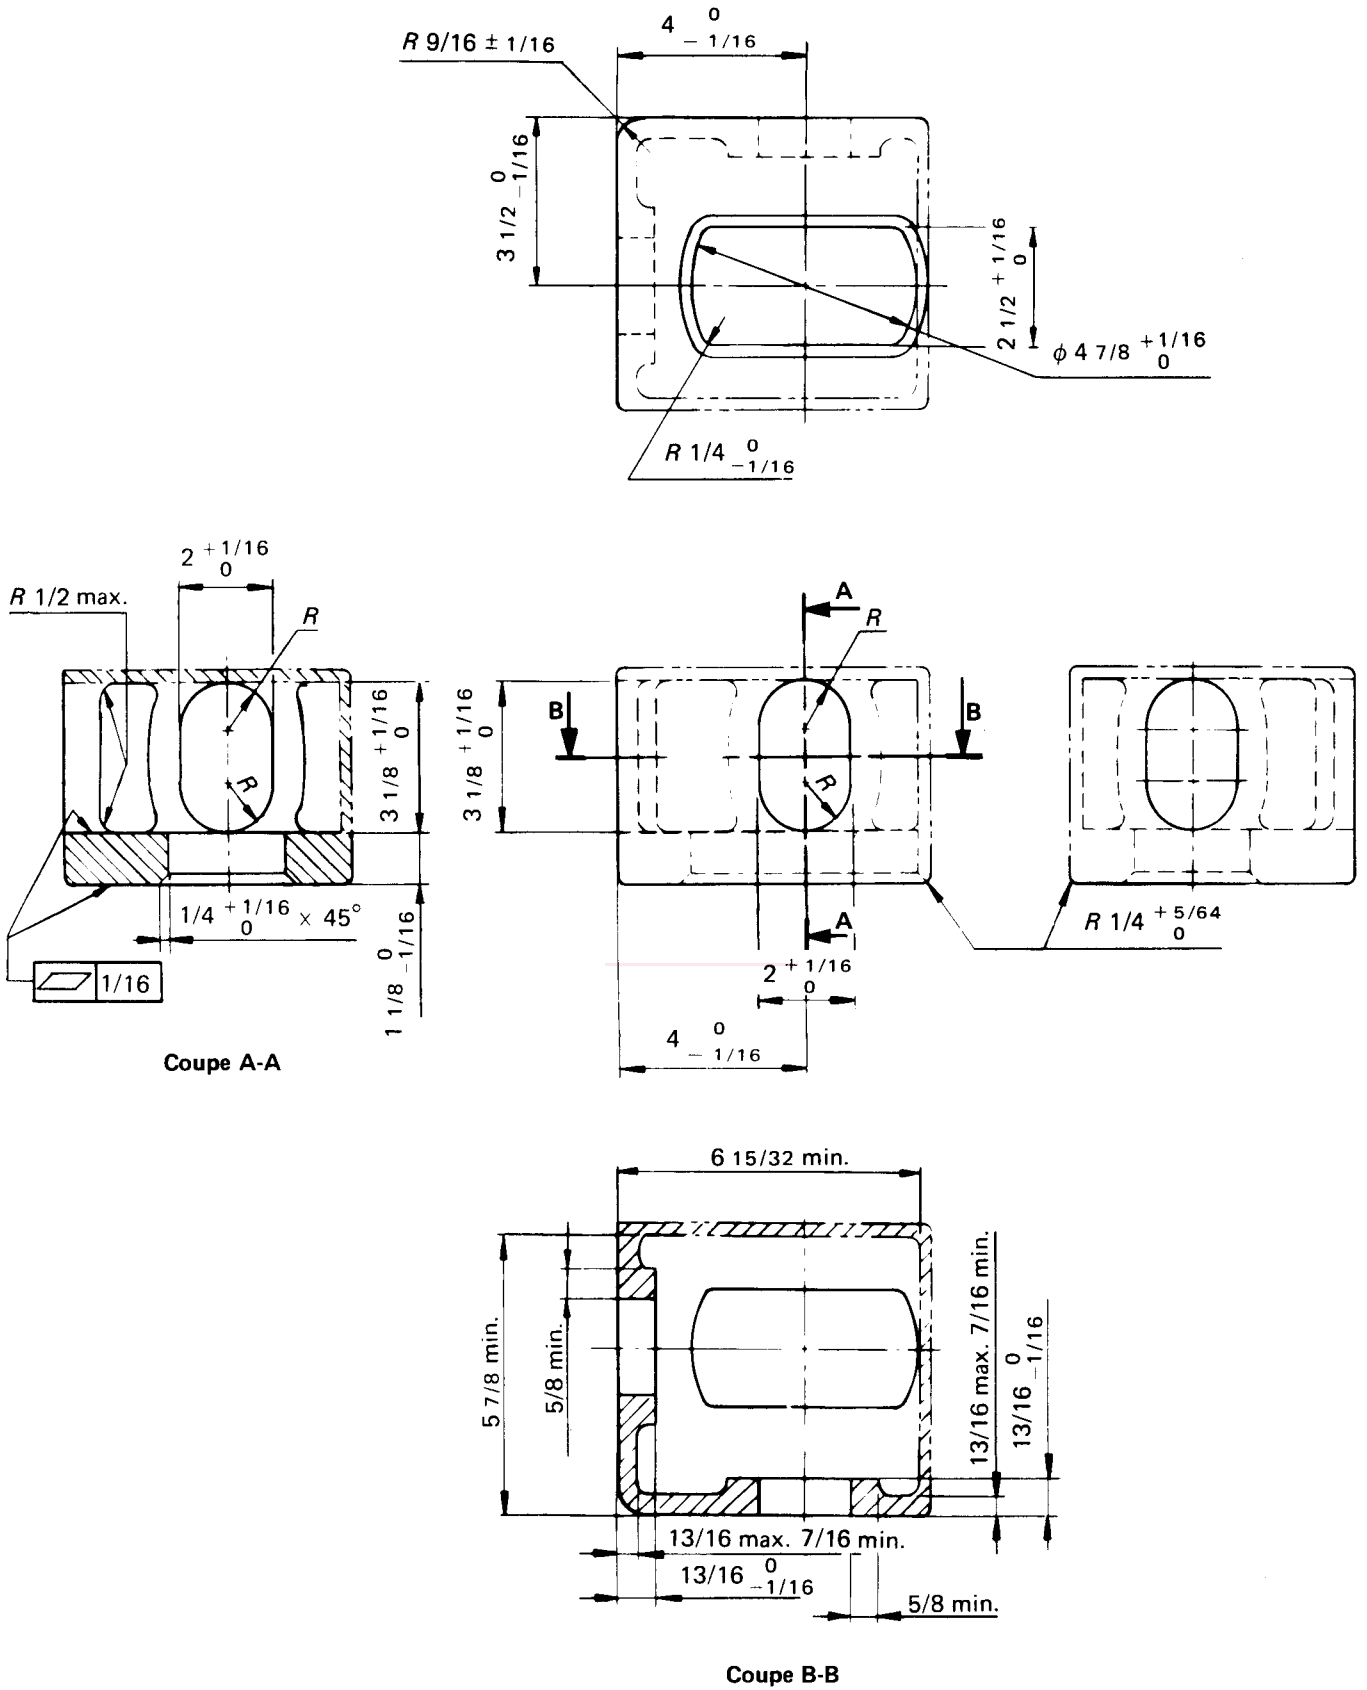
Pièce de coin supérieure — Dimensions en inches
